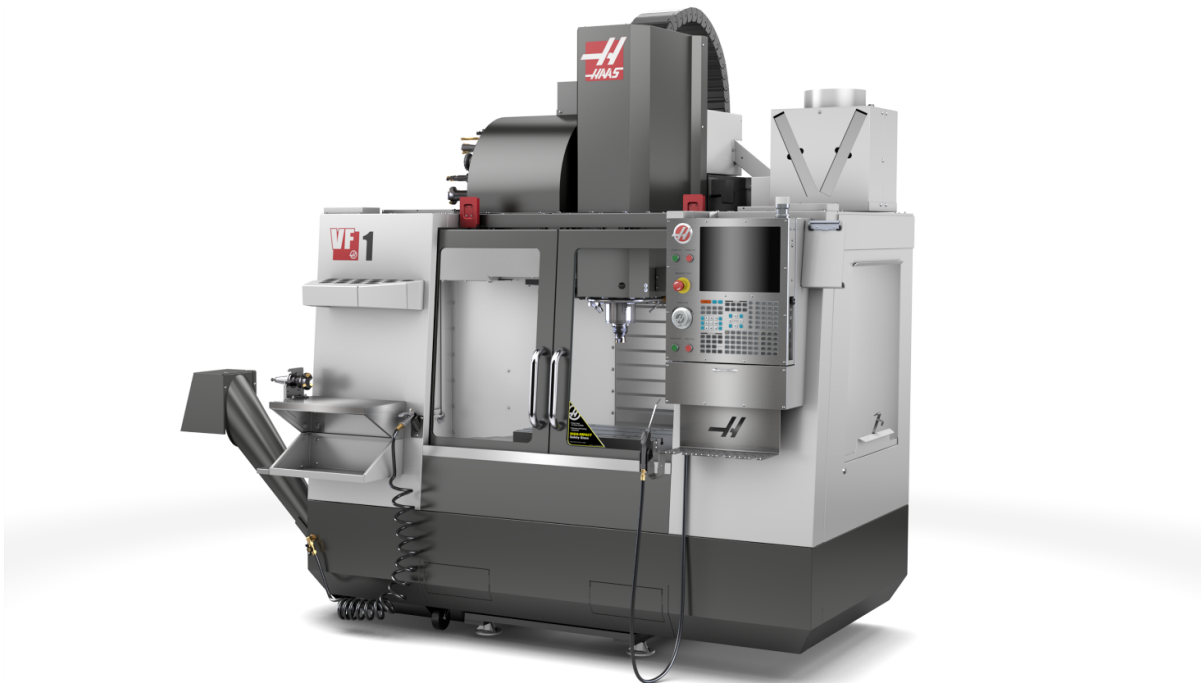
Оброблюючий центр VF-1 (Haas)
